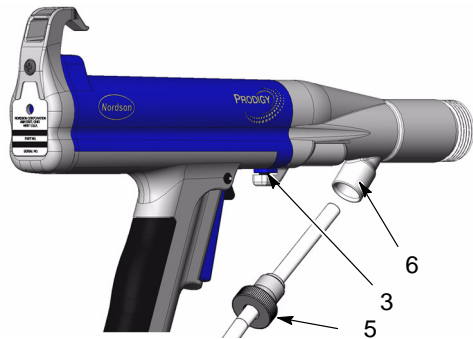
Desserrage de la vis de blocage de l'adaptateur
